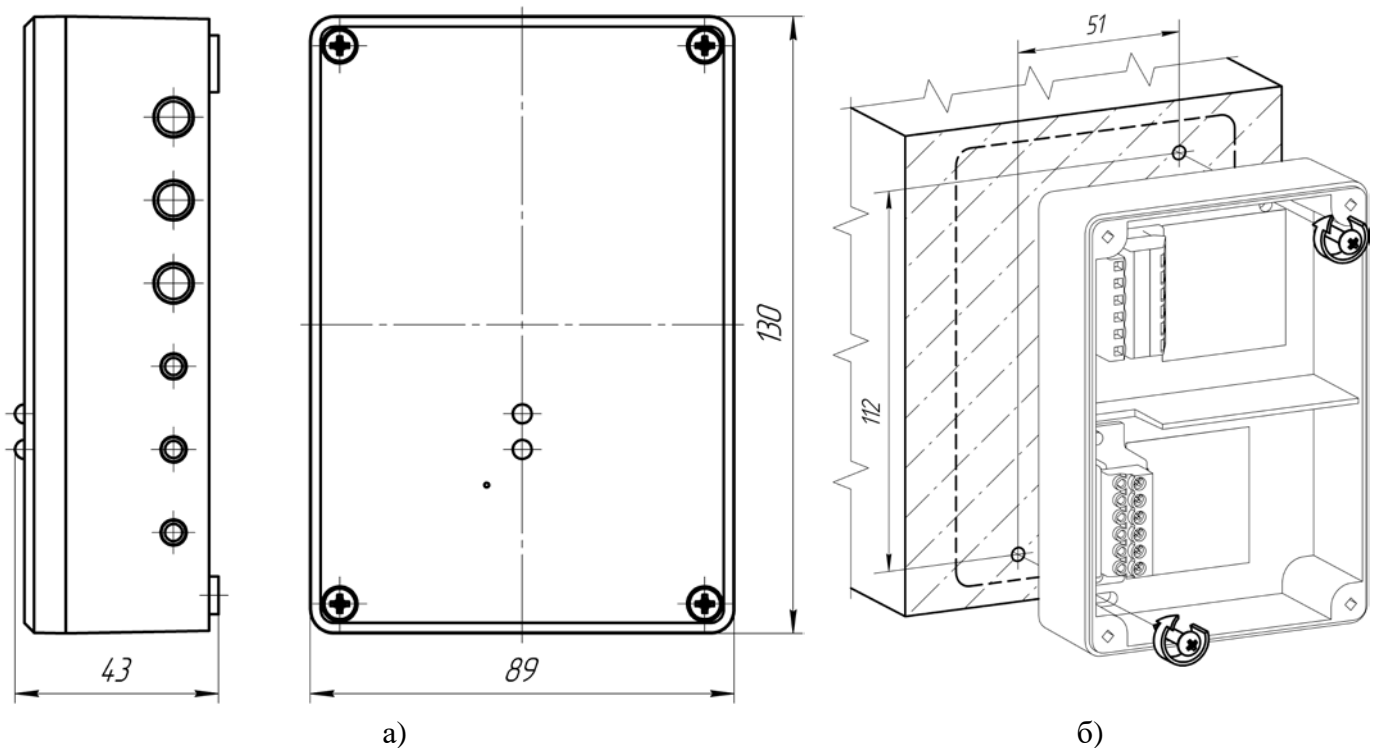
Внешний вид и габаритные размеры (а), установочные размеры (б) блока, размеры в мм.
